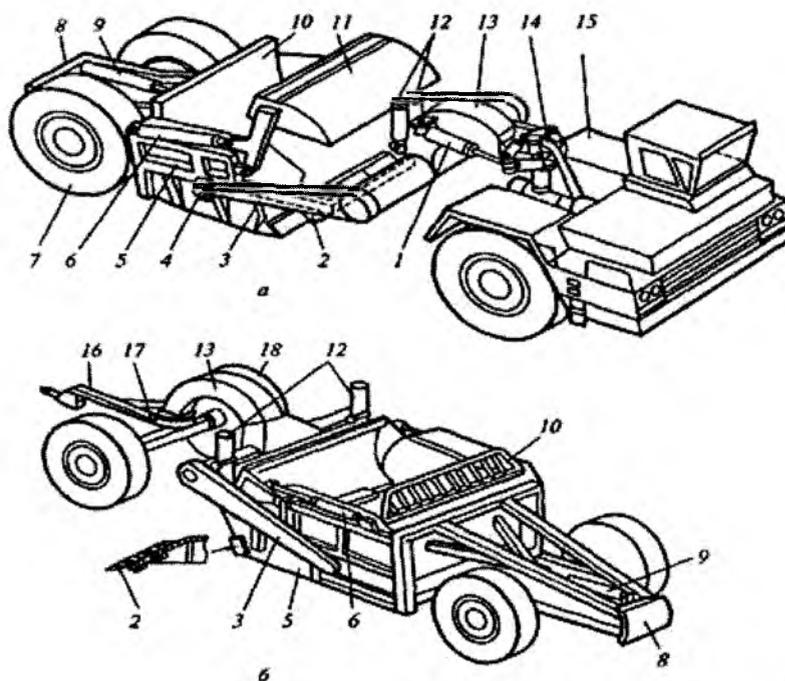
Принципиальные схемы скреперов со скребковым конвейером: а набор грунта; б - выгрузка грунта
